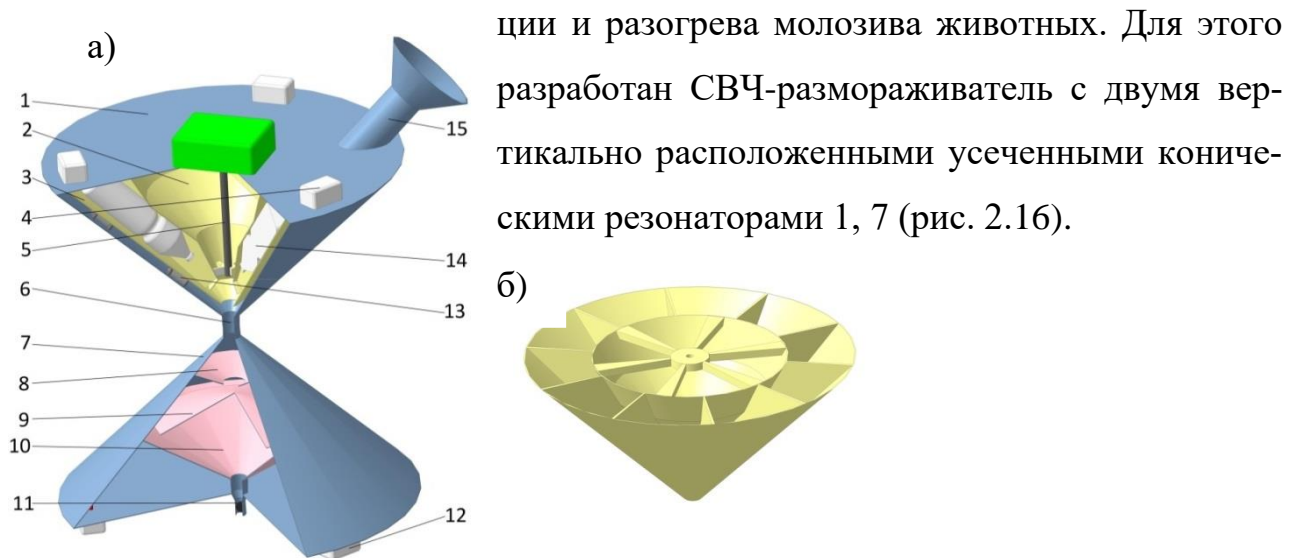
СВЧ-размораживатель непрерывно-поточного действия с коническими резонаторами с состыкованными вершинами для дефростации и разогрева молозива животных: а) общий вид установки в разрезе; б) диэлектрический контейнер с отсеками; 1 – верхний усечённый конический резонатор; 2, 3 – диэлектрический контейнер; 4, 12 – магнетроны; 5 – диэлектрический вал; 6 – цилиндрическая неферромагнитная муфта; 7 – нижний усечённый конический резонатор; 8 – диэлектрическая направляющая в виде усеченного конуса; 9 – диэлектрическая коническая направляющая; 10 – диэлектрический конический накопитель; 11 – шаровой кран; 13 – опорные ролики, 14 – замороженное сырье; 15 – запредельный волновод
